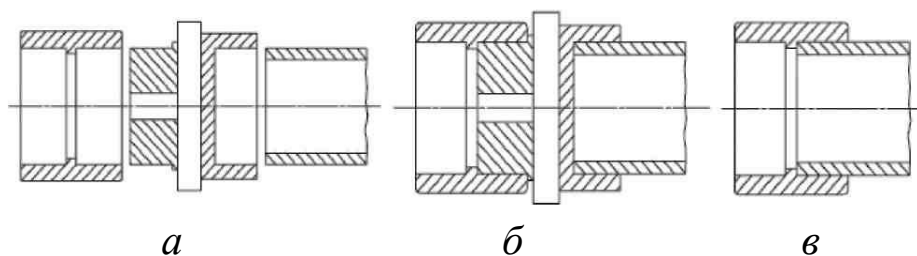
Раструбная сварка: *а* – подготовка к сварке; *б* – выравнивание и прогрев; *в* – соединение и охлаждение
